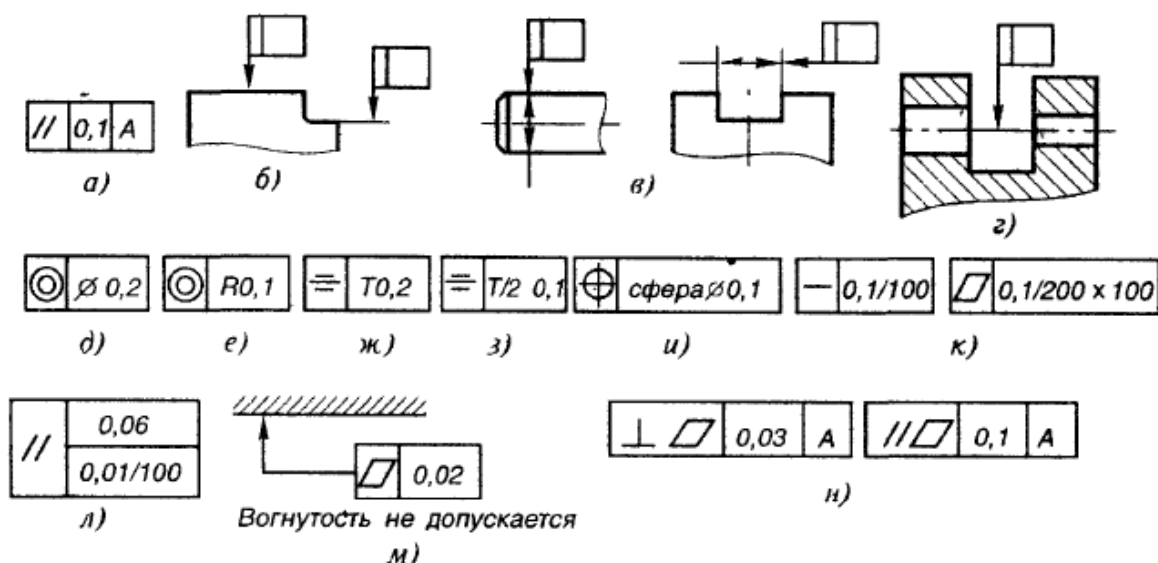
Схемы указания допусков формы и расположения поверхностей
